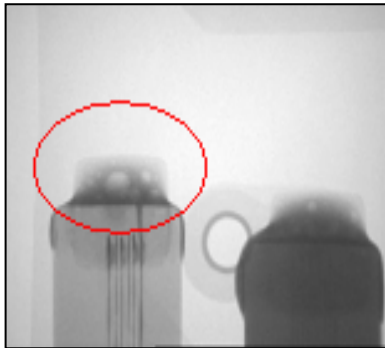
Radiografía que muestra el problema de burbuja en soldaduras.
